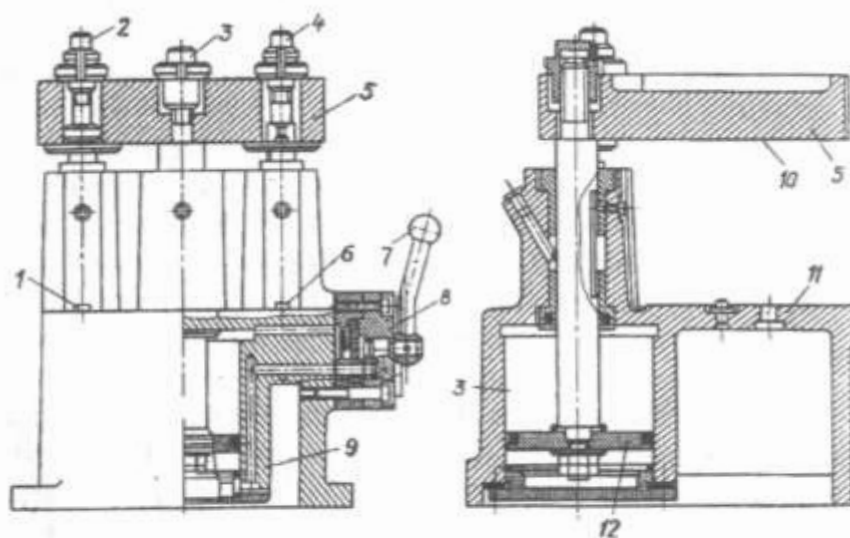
Нормализованный скальчатый кондуктор консольного типа с встроенным пневматическим приводом
